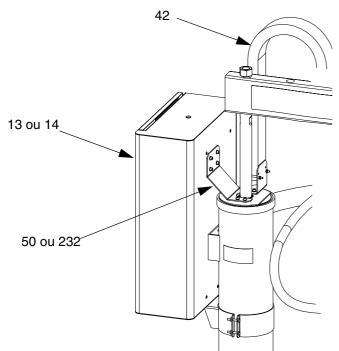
Remplacement des joints d'étanchéité de la tige
